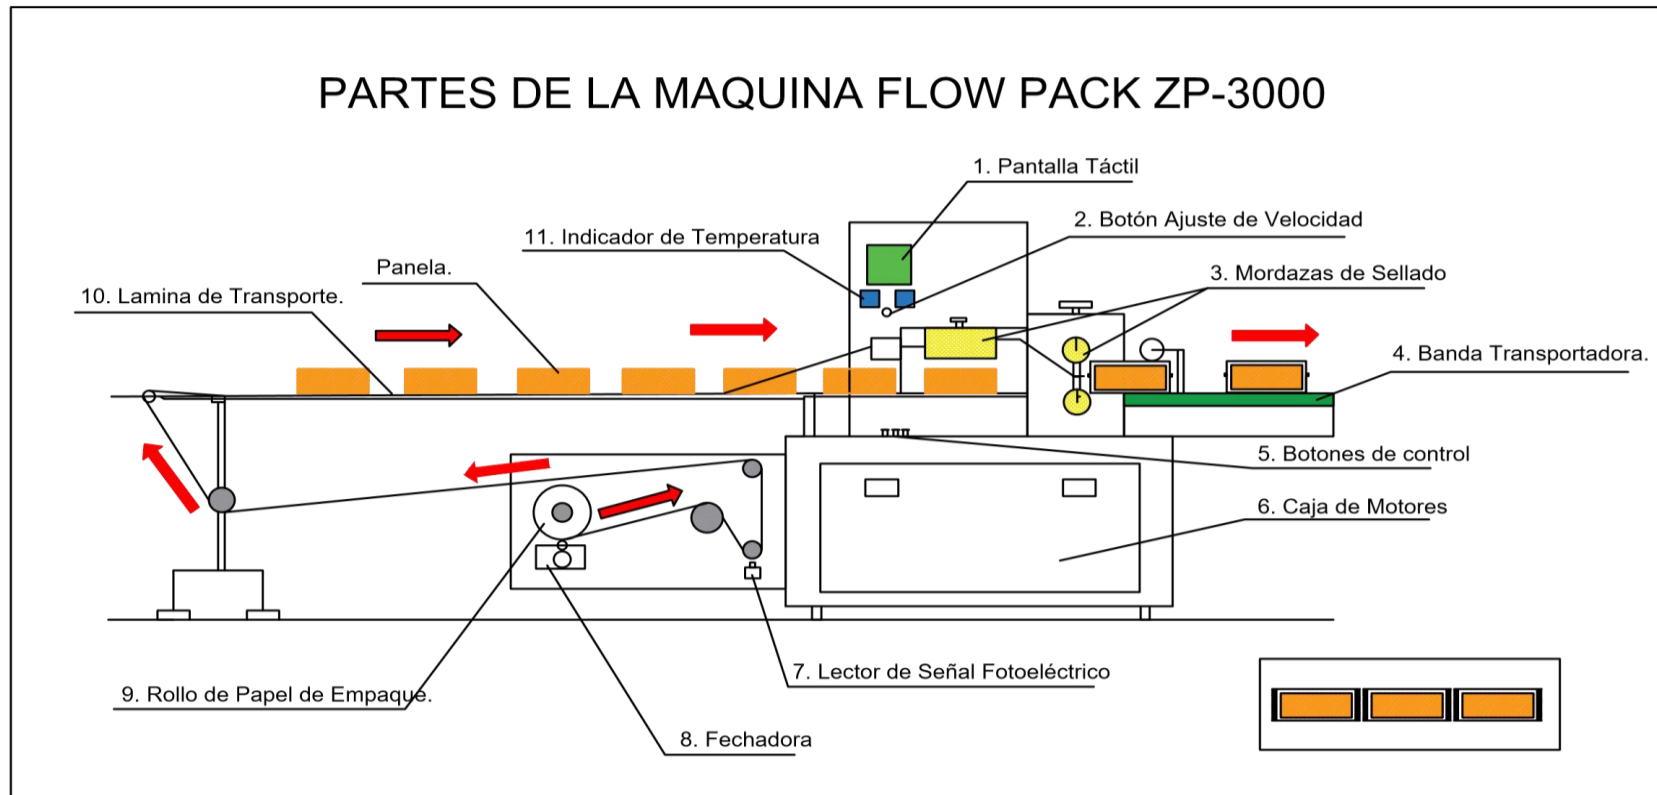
Partes de la Maquina FLOW PACK zp-3000
